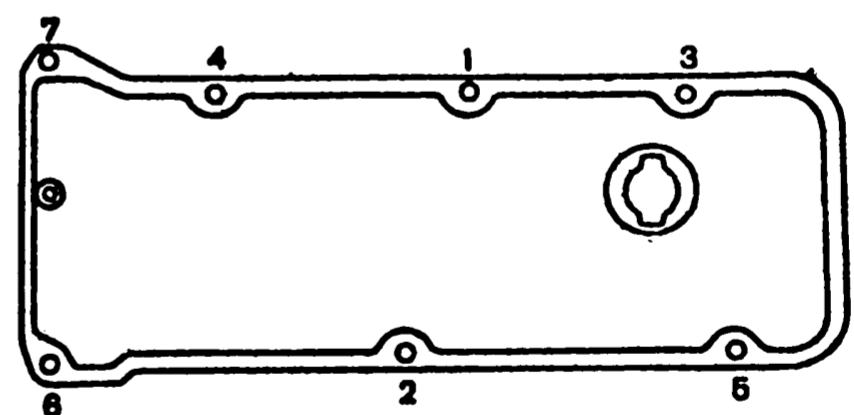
Порядок затягивания гаек крепления крышки головки цилиндров
